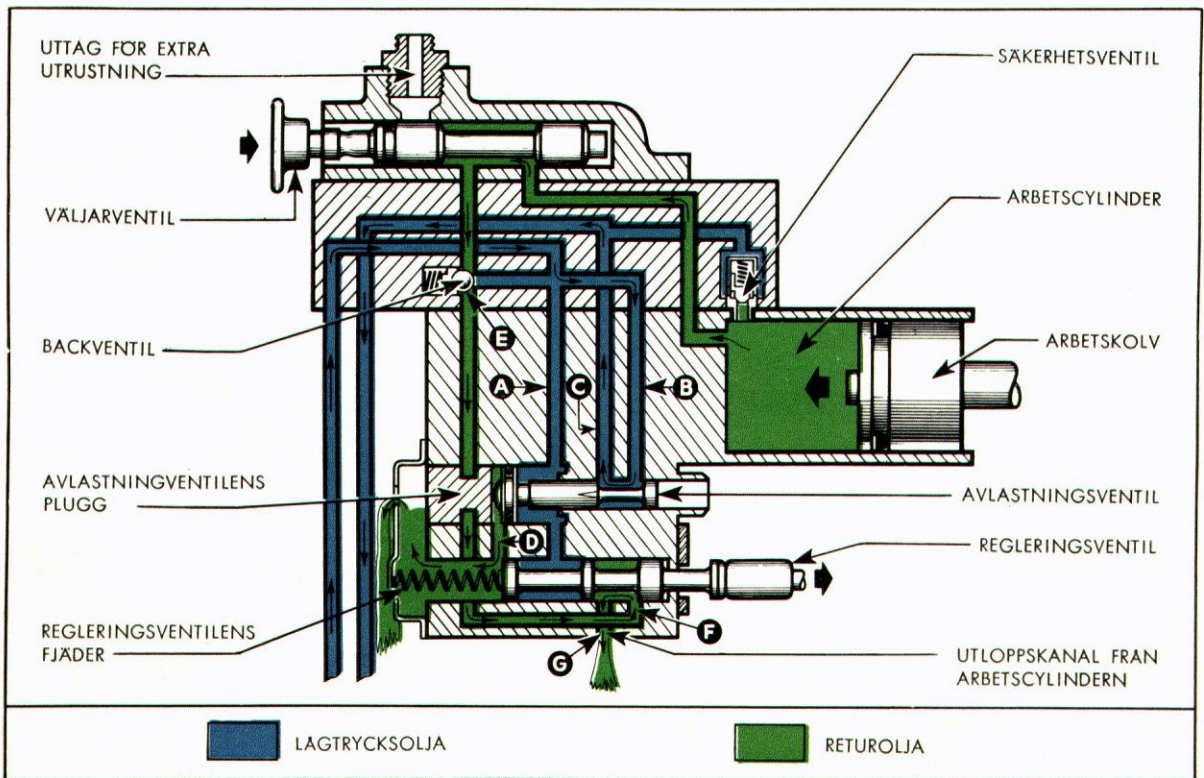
Hydrauliska systemets oljeflöde — sänkning.
